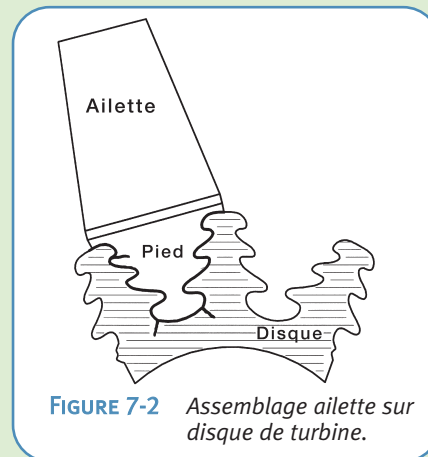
Assemblage ailette sur disque de turbine.
